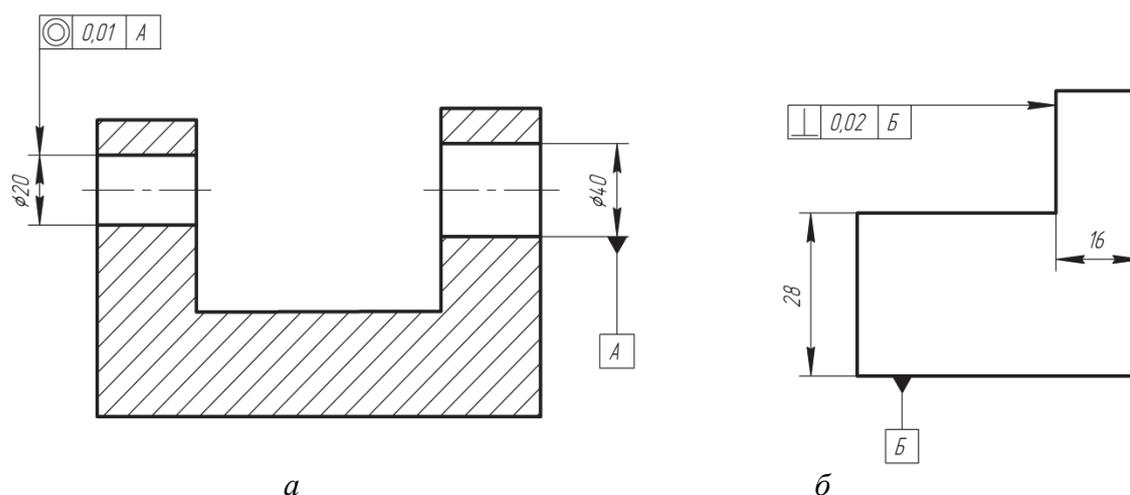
Примеры обозначения допусков расположения:
